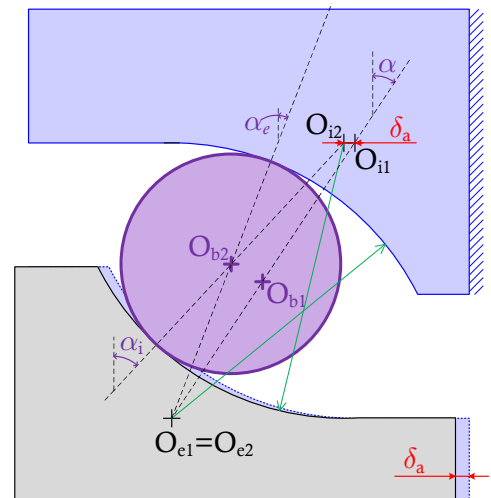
Coupe B-B du roulement par le plan de position angulaire ψ_j .
